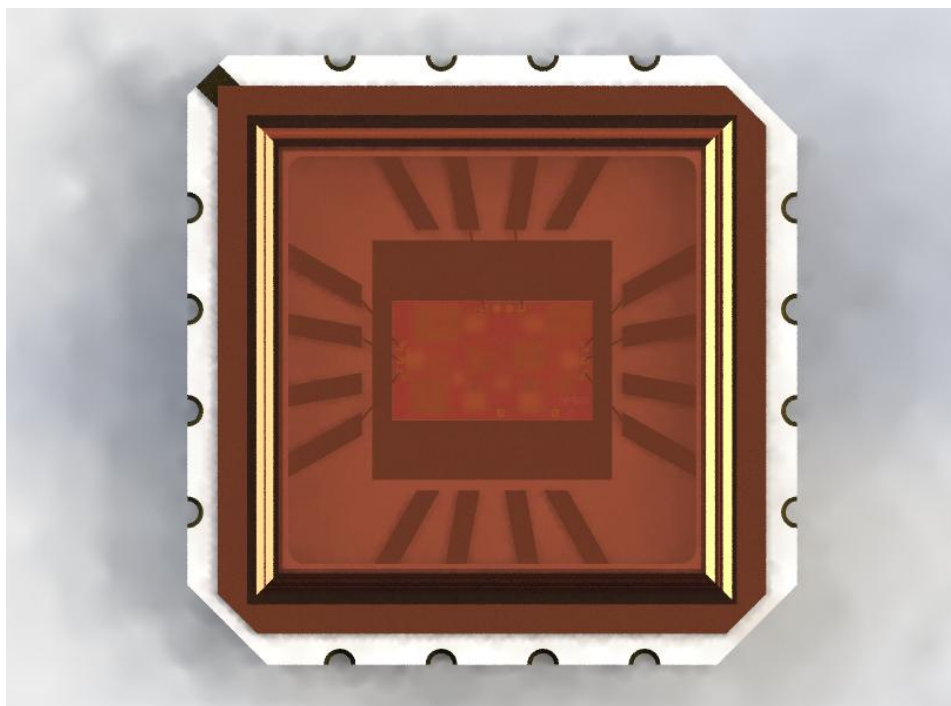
Корпус МИС Micran MP502 (вид сверху)
